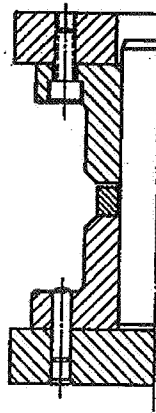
M. Milerinin ( Führungların ) kalıplardaki
